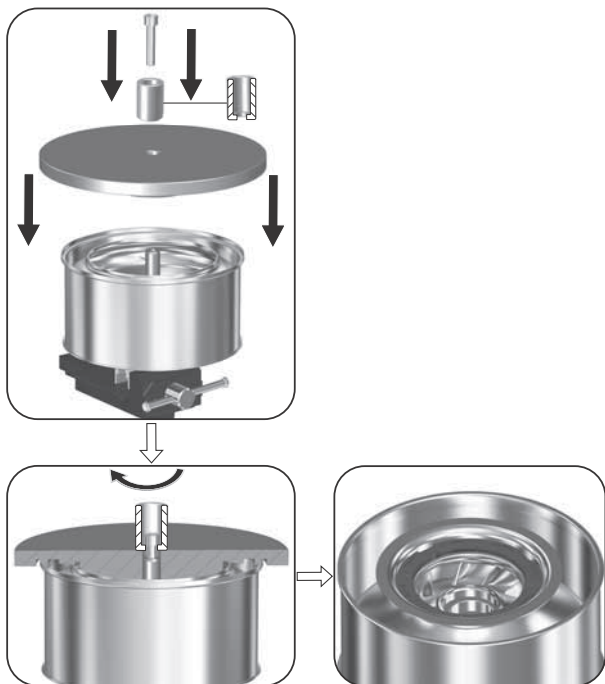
Уплотнительное кольцо, стопор уплотнительного кольца и камера, установленные в приспособлении L.
